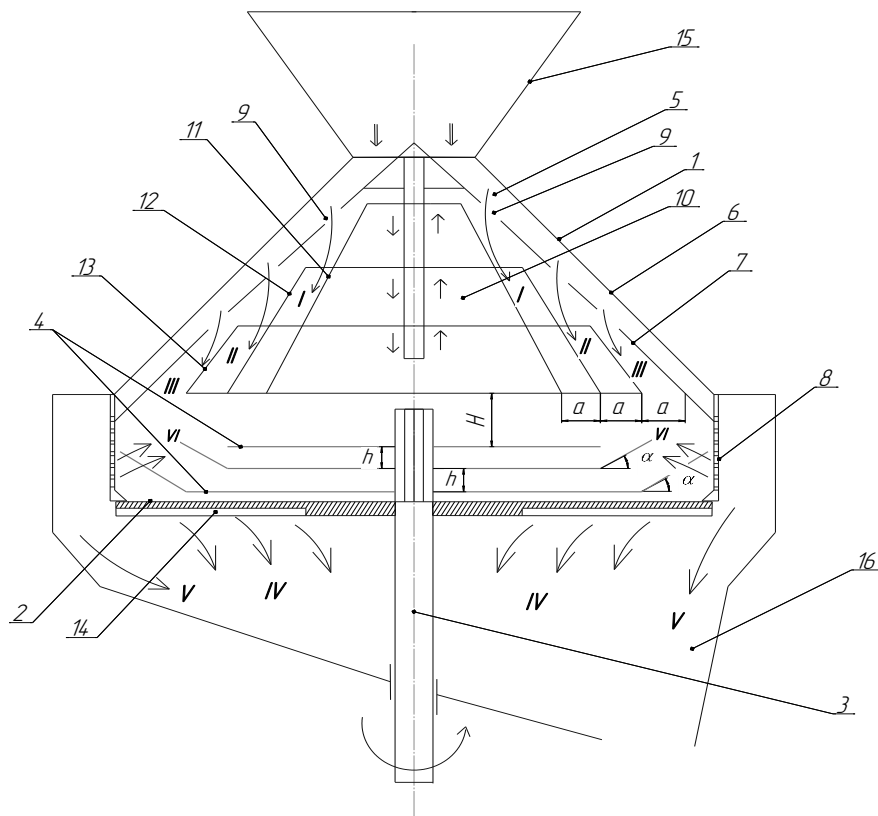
Схема розробленої конструкції камери подрібнення дробарки зерна прямого удару: 1 - корпус; 2 - диск; 3 - вал; 4 - робочі елементи у вигляді тонких стрижнів; 5 - живильний бункер; 6 - конус зовнішній; 7 - конус внутрішній; 8 - циліндрична перегородка; 9 - щілині отвори; 10 - розподільник фракцій; 11, 12, 13 - набір суцільних конусів; 14 - канали клиноподібної форми; 15 - бункер-дозатор; 16 - вихідний патрубок.
